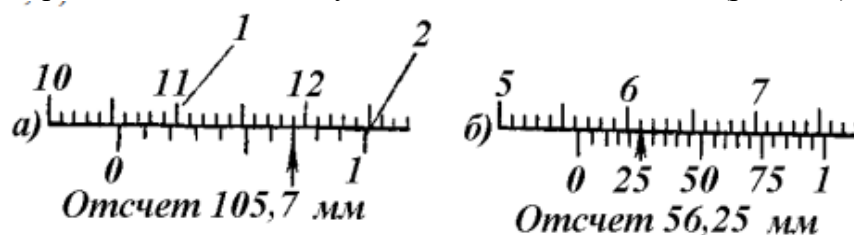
Примеры отсчета размеров по нониусу штангенинструмента: 1 – основная шкала; 2 – шкала нониуса
